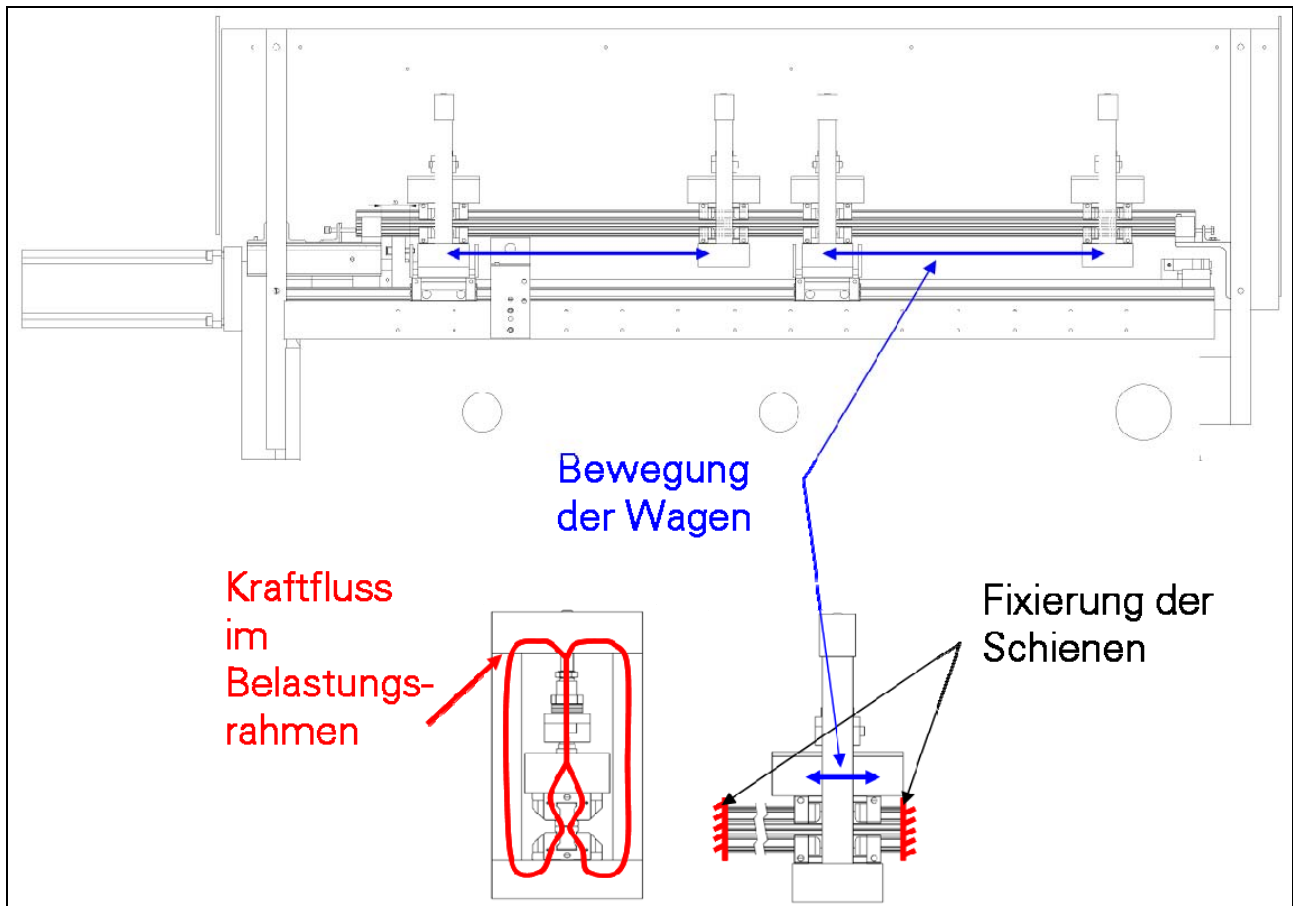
Ausführungsbeispiel Prüfstand mit bewegten Wagen
